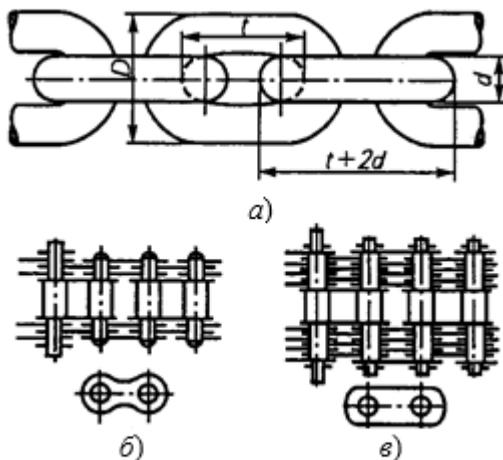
Грузовые цепи: а – сварная; б, в – пластинчатые; t – шаг цепи
